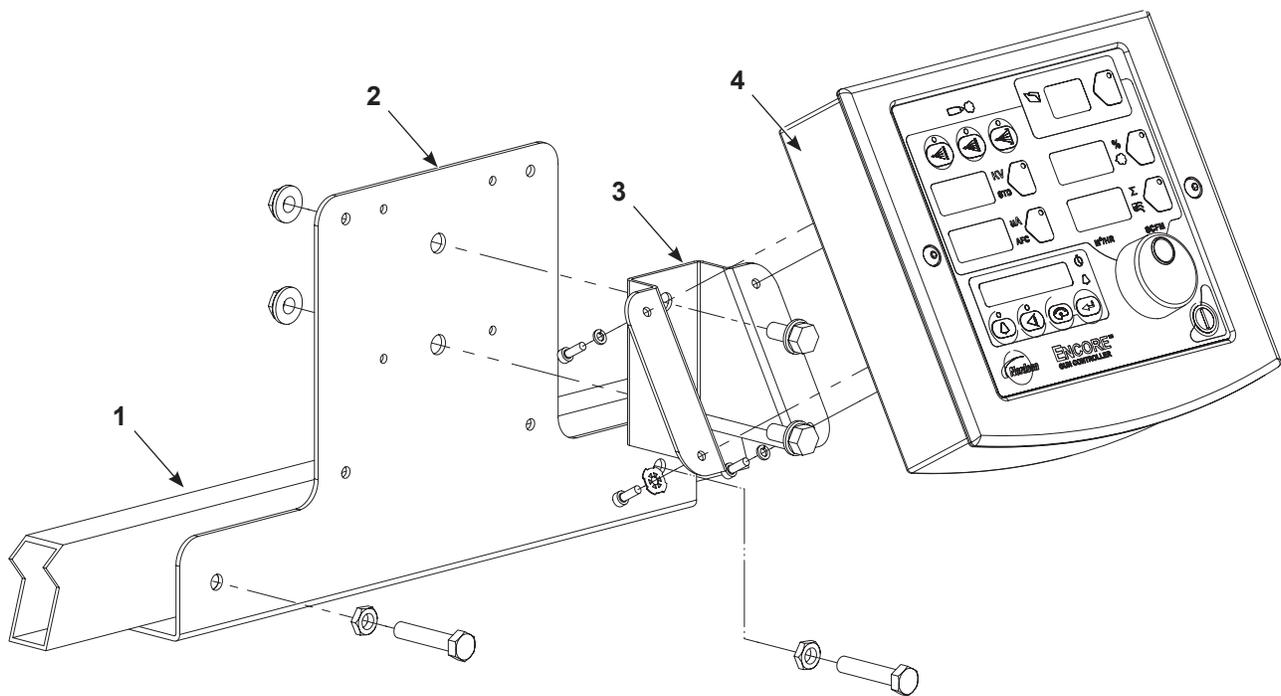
Installation avec montage sur rail du contrôleur (orientation de bas en haut)
